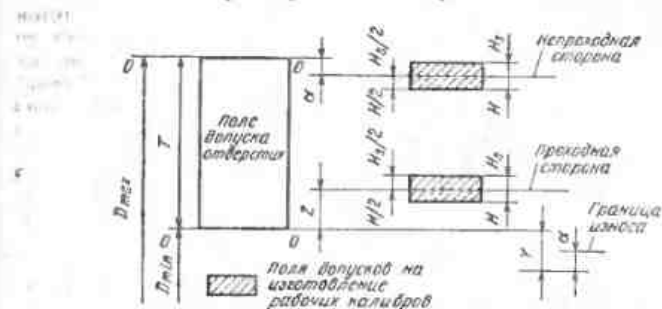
Схема расположения полей допусков калибров для отверстий
